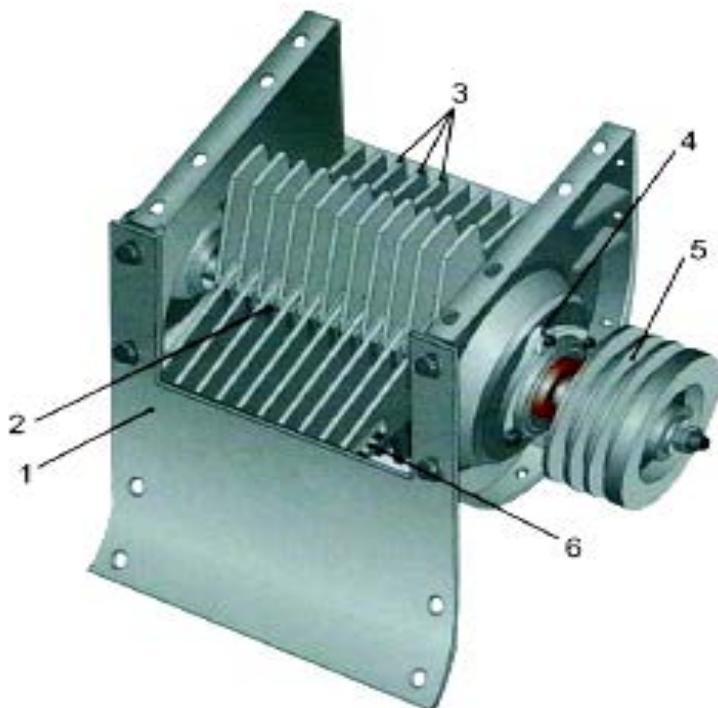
Доизмельчитель зерна: *1* – корпус; *2* – ротор; *3* – ножи; *4* – опора с подшипником; *5* – шкив привода ротора; *6* – балансировочная пластина
